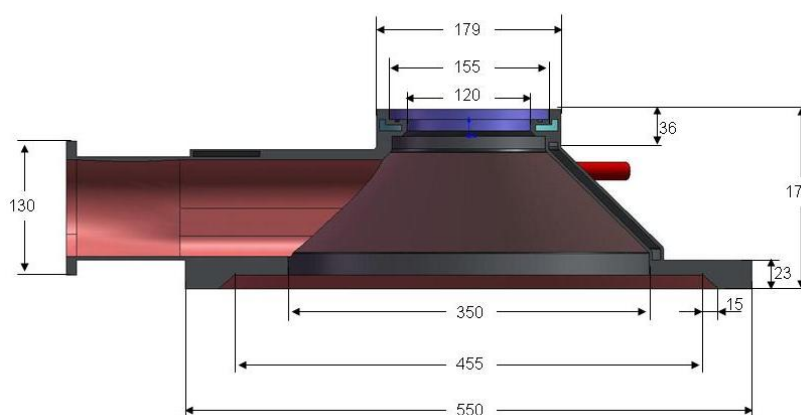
Pormenor da flange inferior da câmara de vazamento e cotas gerais da câmara de fusão.
